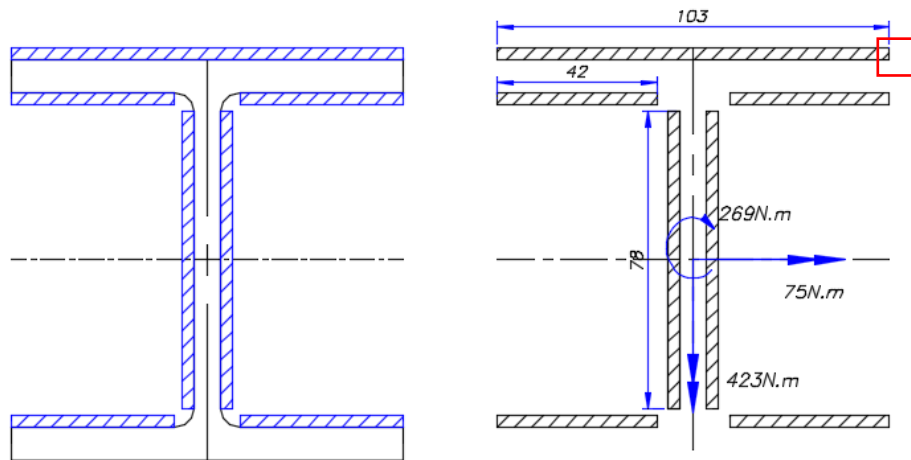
Esquema de la soldadura para los perfiles longitudinales.
